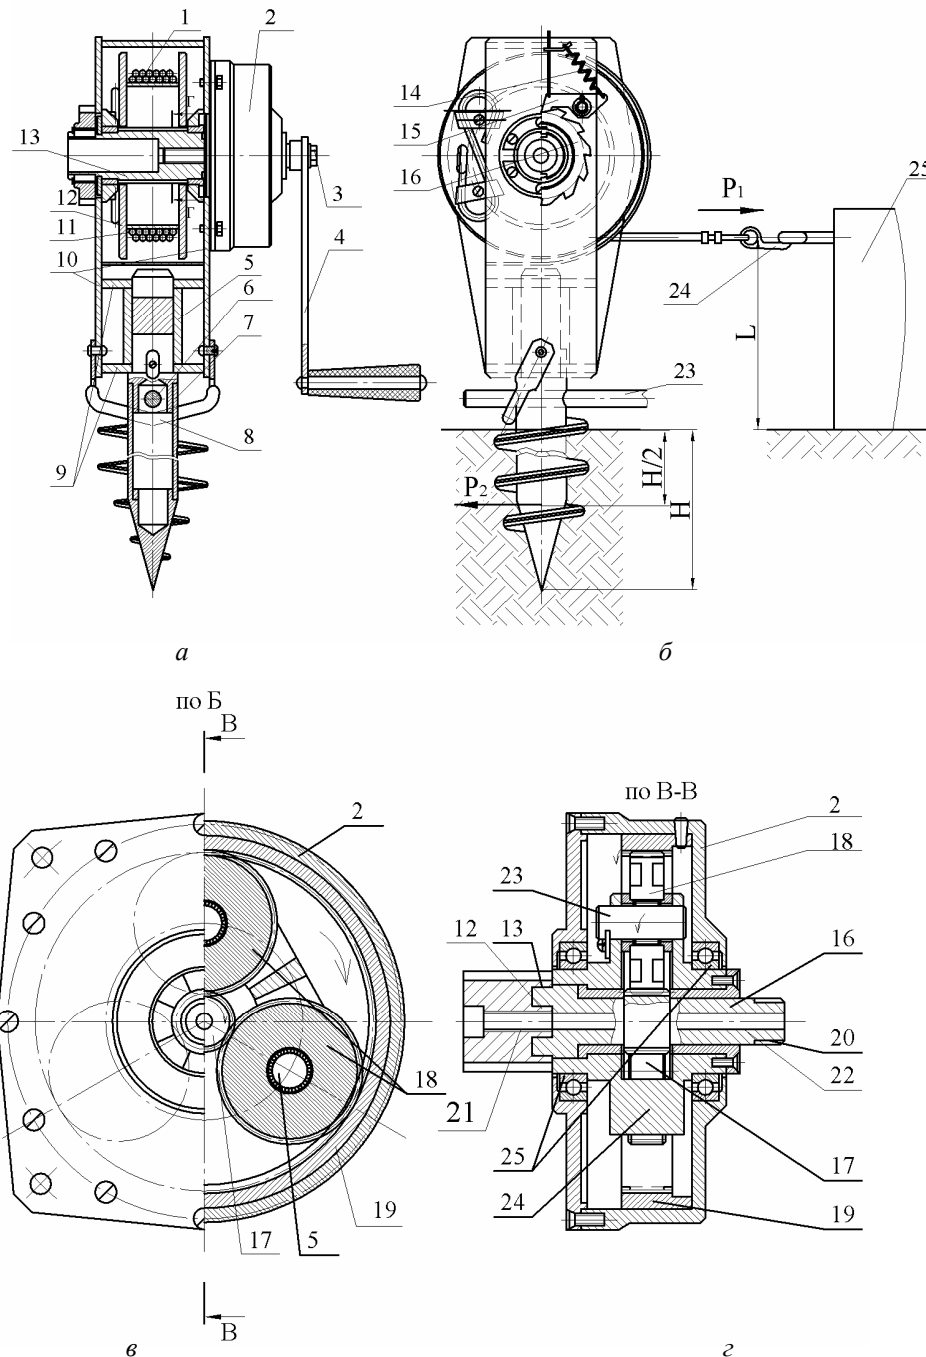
Конструкція гвинтової підіймально-транспортної лебідки (а, б) і циліндричного привідного барабана (в, г): 1 – канат; 2 – корпус редуктора; 3 – стяжний болт; 4 – ручка; 5 – втулка; 6 – палець; 7 – гвинтова опора; 8 – вантажна скоба; 9 – горизонтальні перегородки; 10 – видовжені пластини; 11 – привідний барабан; 12 – храпова втулка; 13 – пружина; 14 – храпова собачка; 15 – храпове колесо; 16 – стрижень
